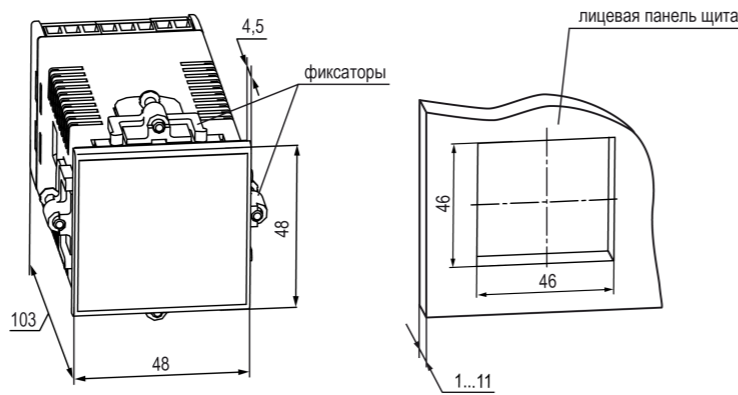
Габаритные размеры корпуса Щ5 и монтажного отверстия в щите
